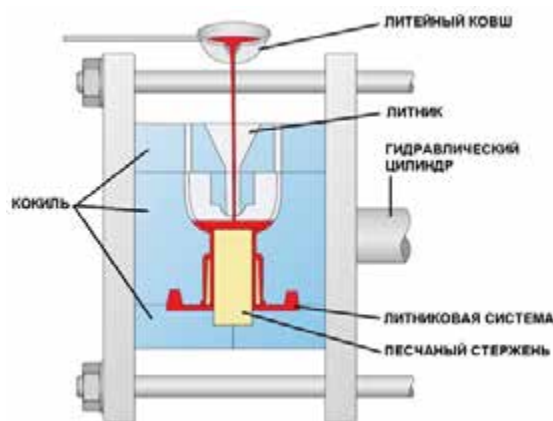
ro-08: Схематическое изображение свободного литья в кокиль под действием силы тяжести металла; источник: MSI
